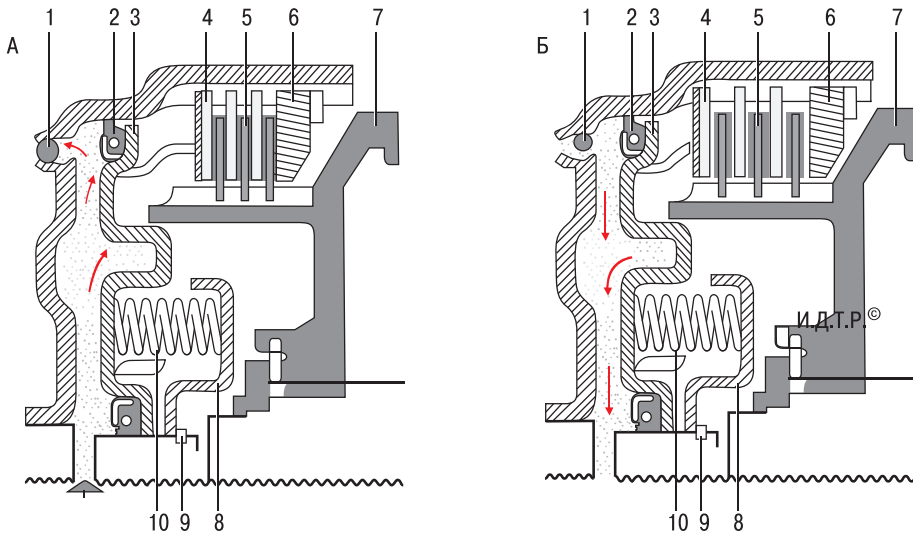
Схема работы многодисковой муфты: А – многодисковая муфта включена; Б – многодисковая муфта выключена; 1 – шариковый клапан; 2 – уплотнительное кольцо; 3 – поршень; 4 – фрикционный диск; 5 – фрикционный диск с накладками; 6 – упорный диск; 7 – ступица муфты; 8 – упор пружины; 9 – стопорное кольцо; 10 – возвратная пружина
